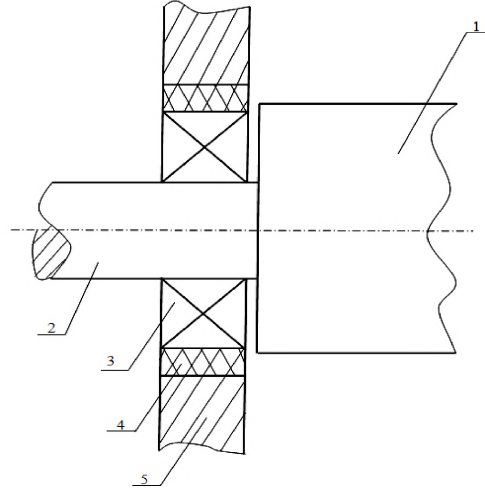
Упругая подшипниковая опора пильного цилиндра
